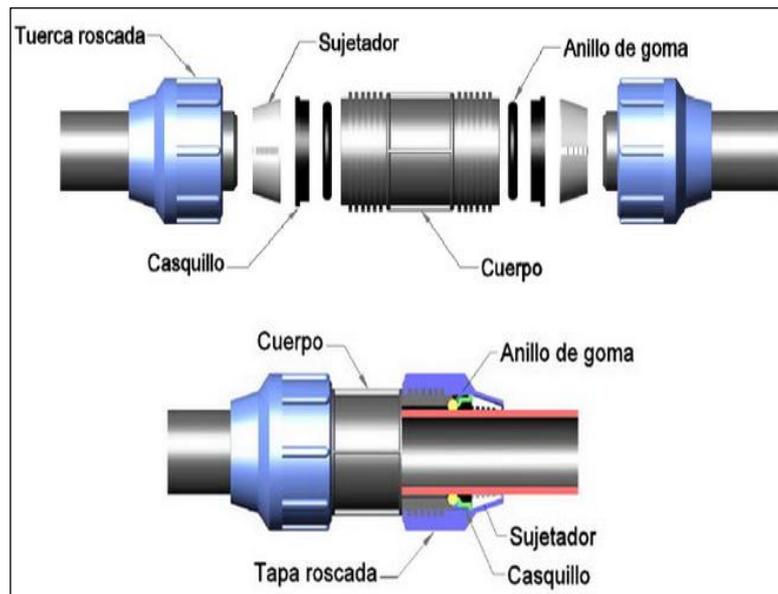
UNIÓN POR COMPRESIÓN. (7)
